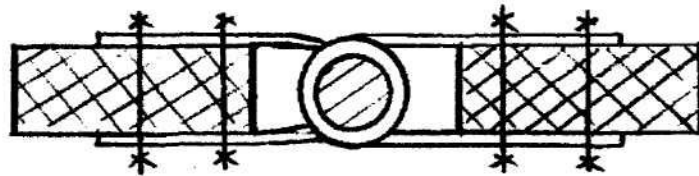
Схема з'єднання кінців стрічки металевими з'єднувачами
